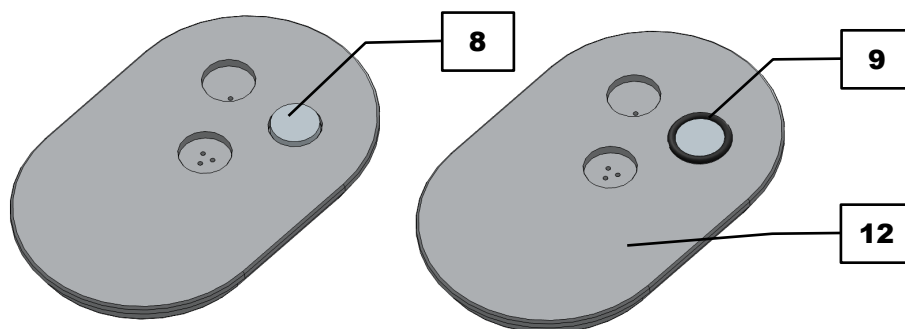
Montaggio di filtro sinterizzato e O-ring
